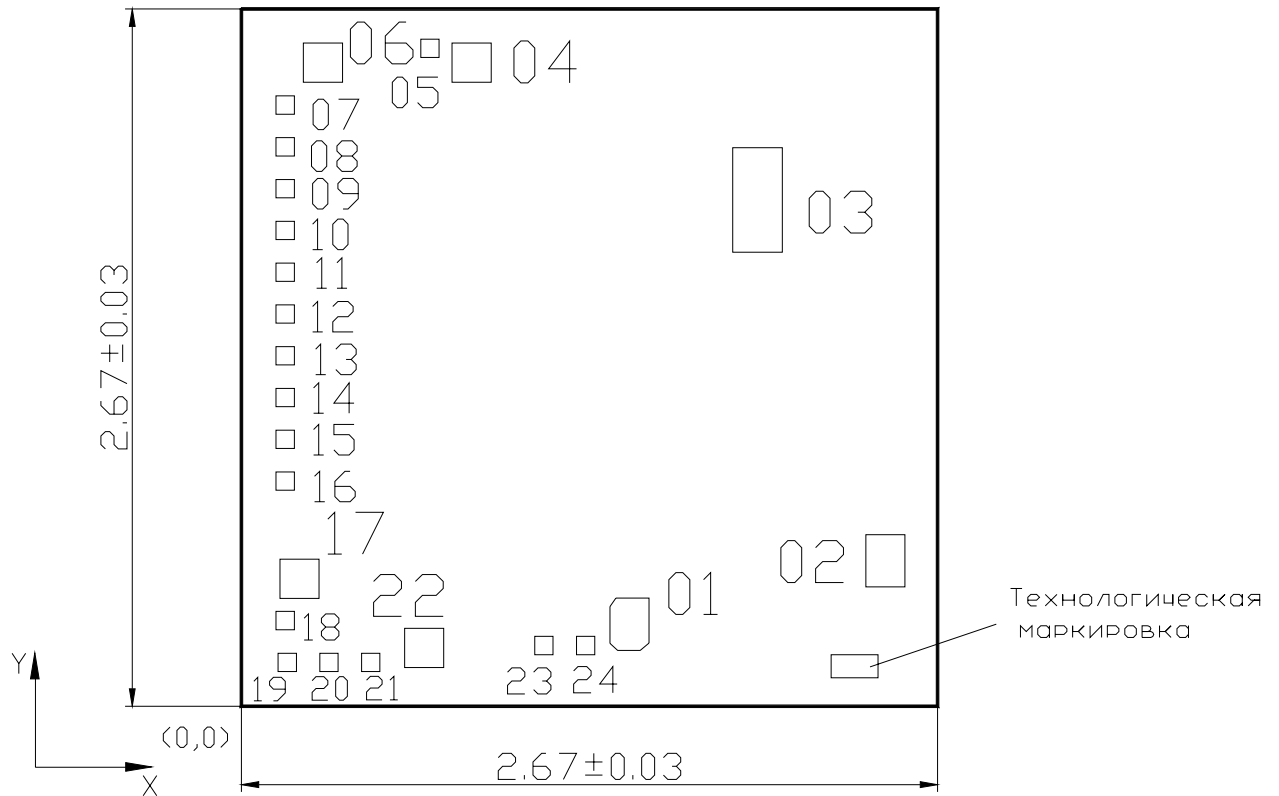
Габаритные размеры корпуса типа 1501.5-4
